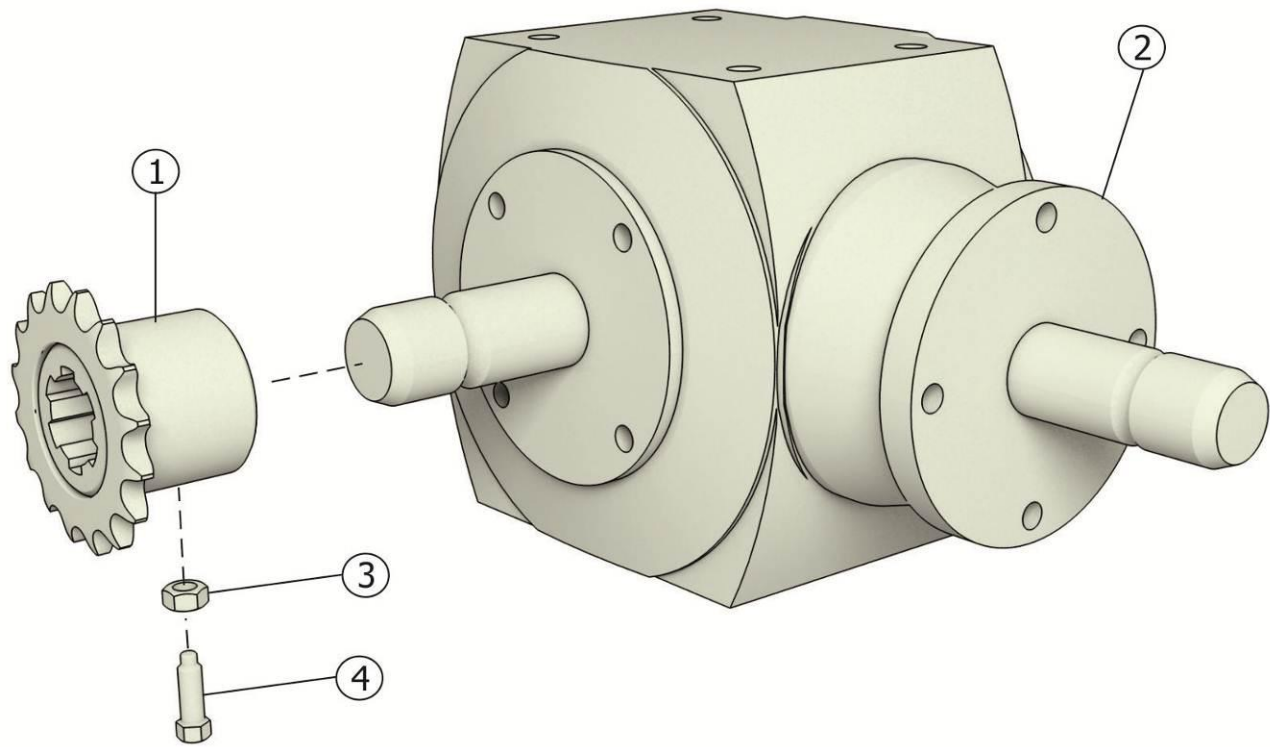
Редуктор ПСП-10МВ.01.01.590А
